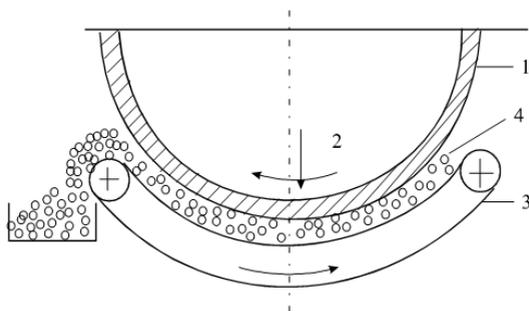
Схема сварки кольцевых швов на флюсо-медной перекатывающейся подкладке: 1 – изделие; 2 – электрод; 3 – гибкая лента; 4 – флюс
